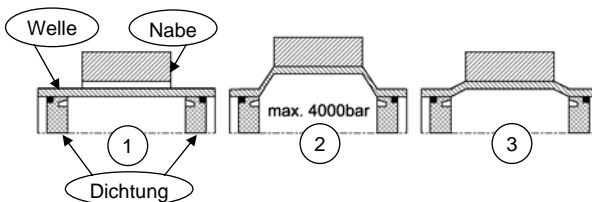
Prinzipskizze des Innenhochdruckfügens einer Welle-Nabe-Verbindung
